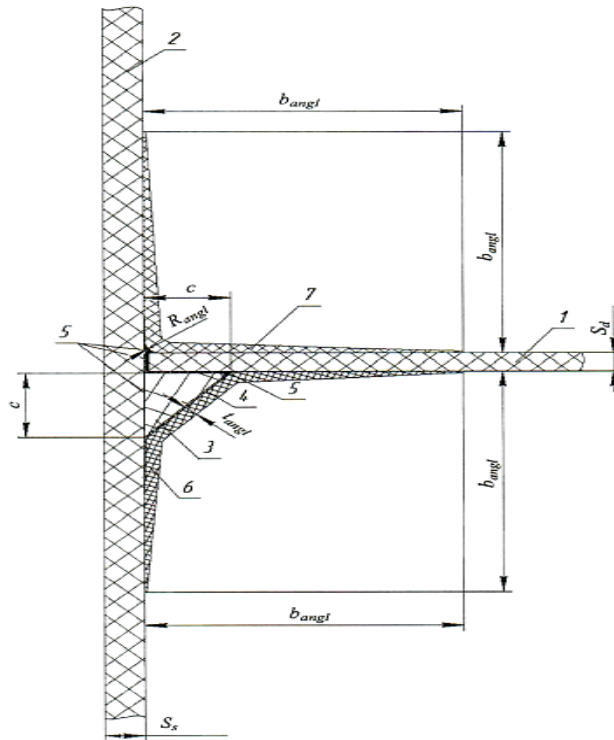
Вузол з'єднання внутрішньої палуби (платформи) з обшивкою борту одношарової конструкції:
